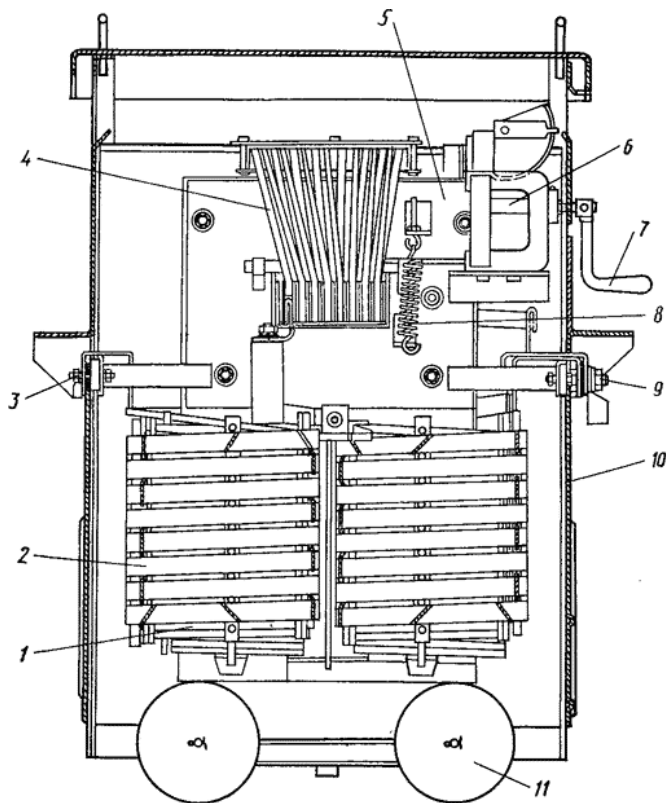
Устройство сварочного трансформатора СТН-500-1
